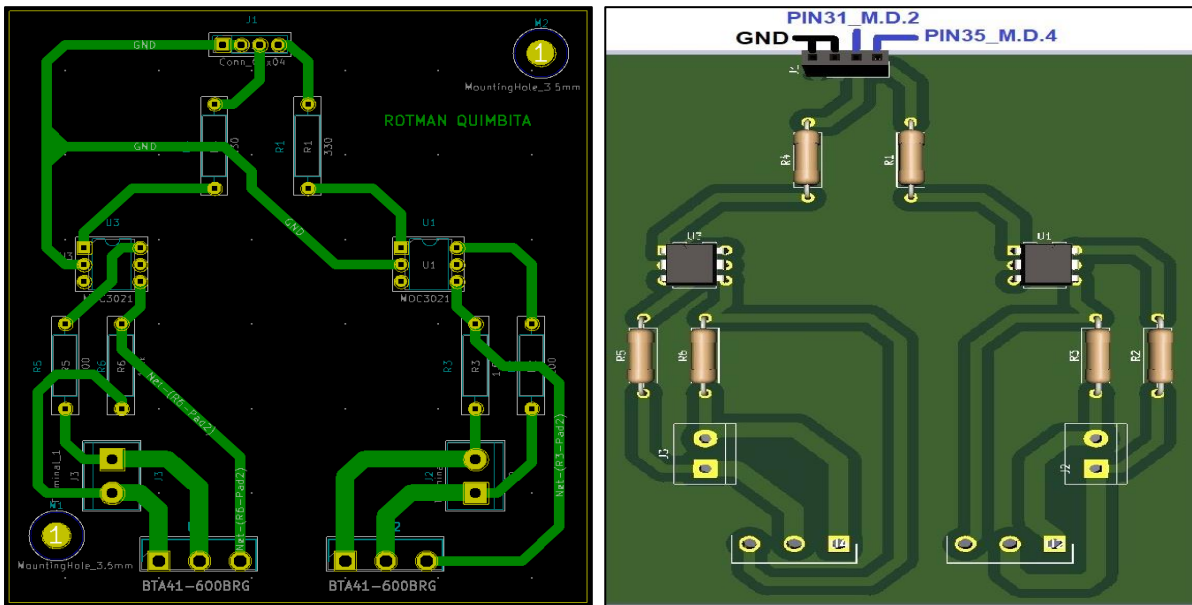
Módulo de disparo 2 y 4 - diseño PCB y visualización 3D.
